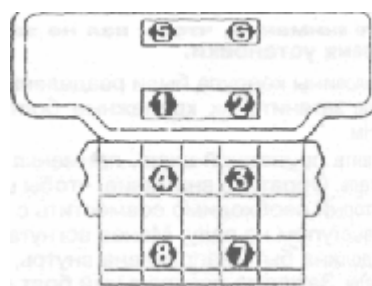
Порядок затяжки крепления подшипников (через нижнюю часть картера) — Двигатель В234F
